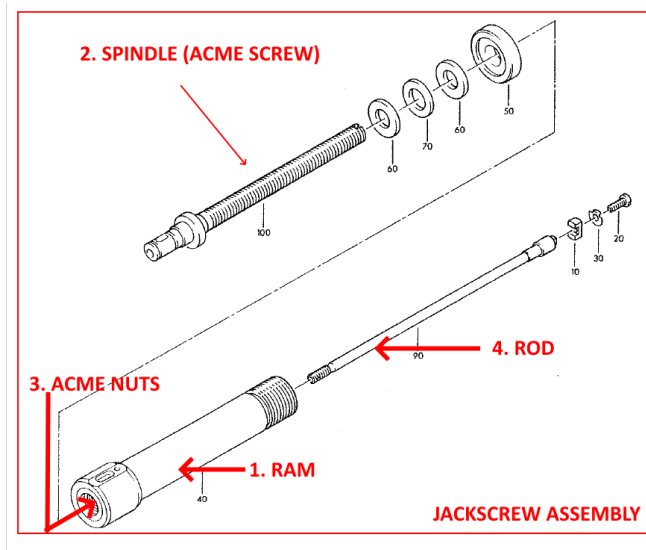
dettaglio dei componenti del *jack screw assembly* (su disegno tratto *EME Pitch trim Actuator 129-1-1100 Series Component Maintenance Manual with Illustrated Parts List*).
